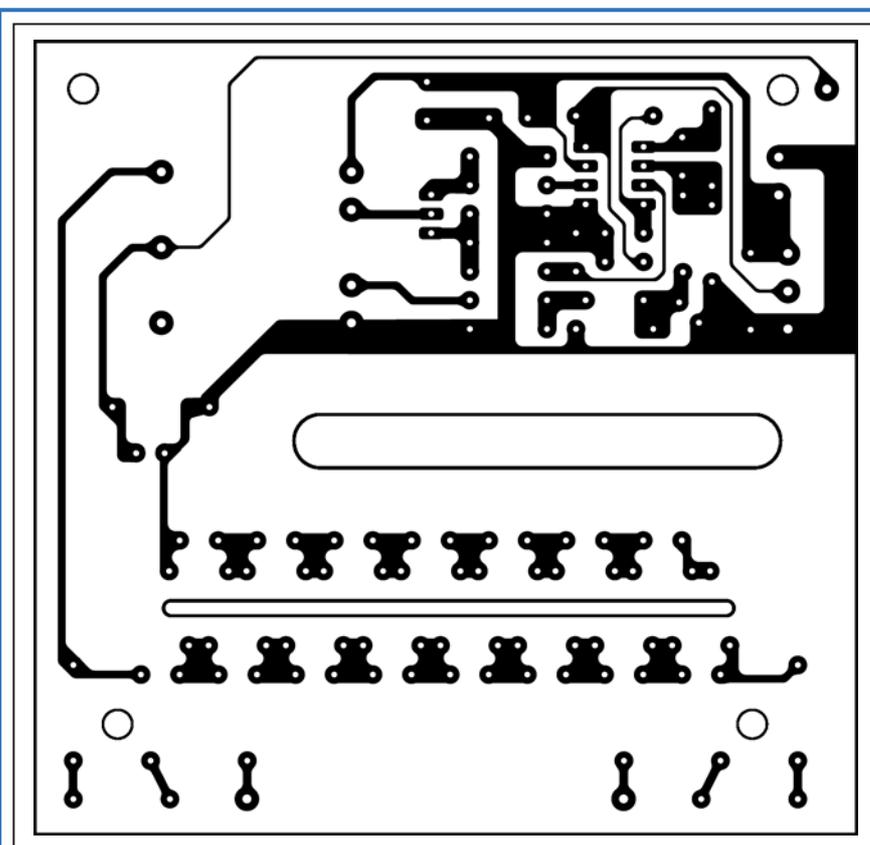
Dessin, à l'échelle 1, de la platine haute tension.
